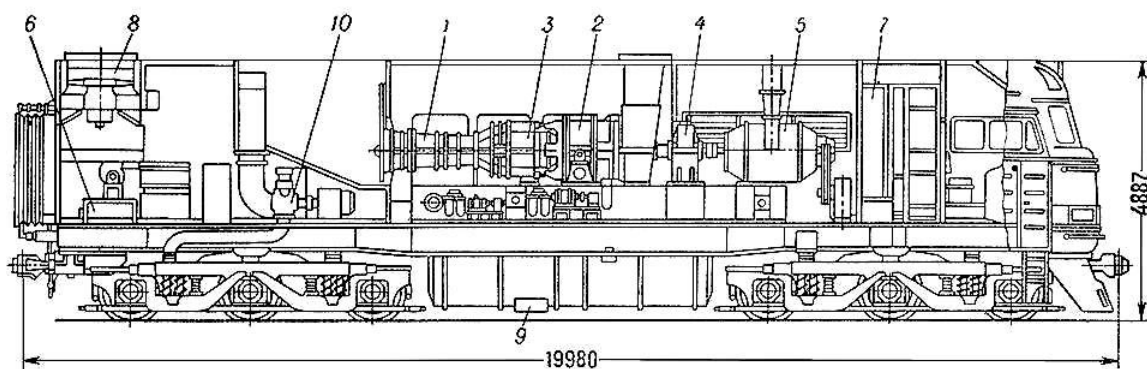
Расположение силового оборудования газотурбовоза Г1-01: 1 – компрессор; 2 – турбина; 3 – камеры сгорания; 4 – редуктор; 5 – главные генераторы; 6 – вспомогательный дизель; 7 – высоковольтные камеры; 8 – холодильник газотурбинного двигателя; 9 – топливный бак; 10 – тормозной компрессор.
